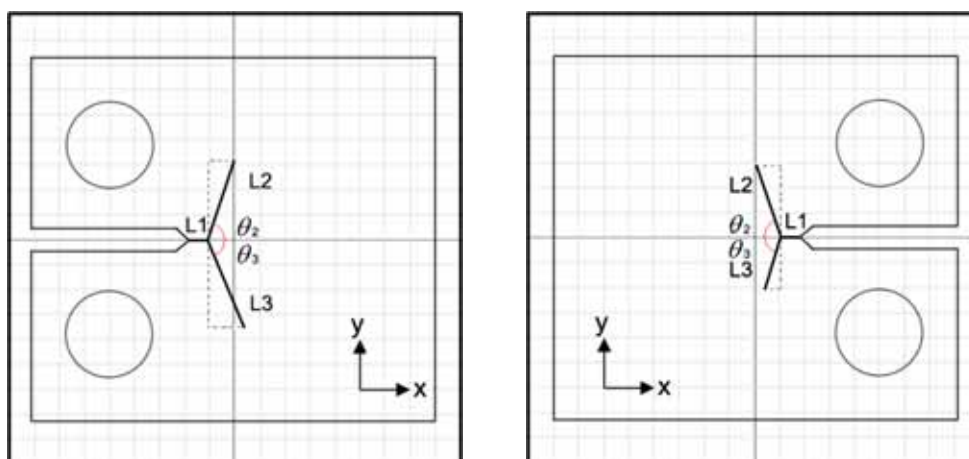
Provete fissurado relativo ao ensaio 3, aço Cr-Mn:
